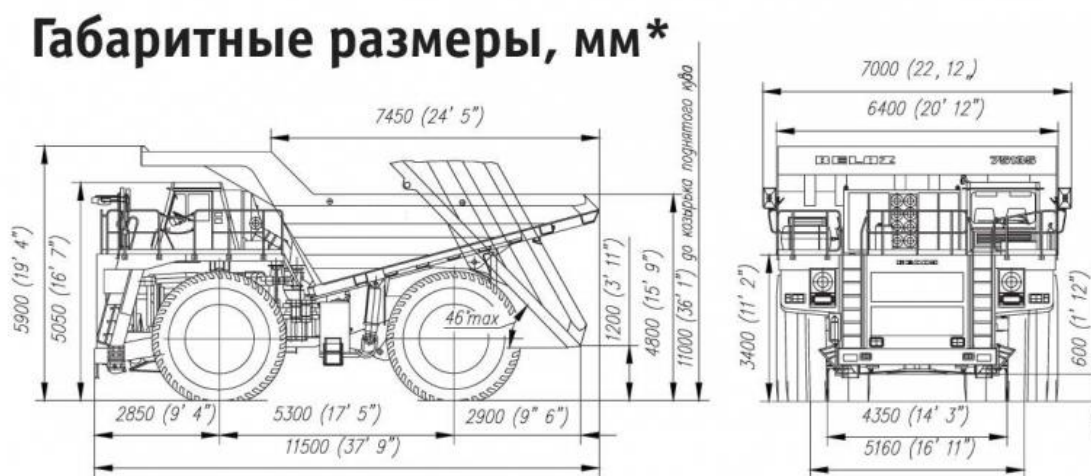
Габаритные размеры автосамосвала БелАЗ 75131
